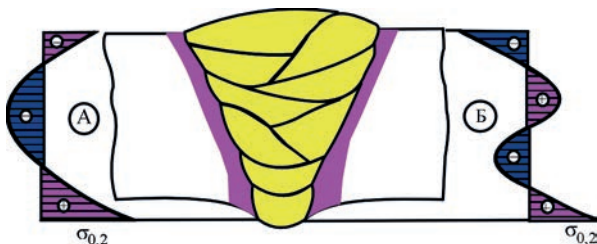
Схемы распределения остаточных напряжений ( $\sigma_y$ ) в ОШЗ сварных соединений, выполненных в несколько проходов (многослойная сварка): стыковое сварное соединение пластин (А), стыковое сварное соединение трубопровода 325×16 мм из стали 08Х18Н10Т (Б)
